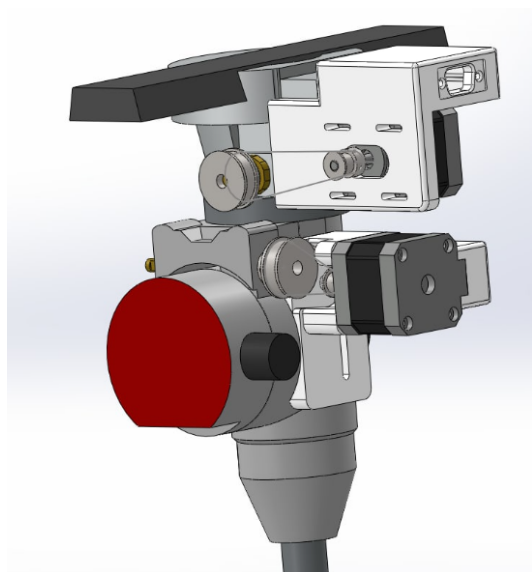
Поворотный механизм с шаговым двигателем и зубчато-ременной передачей
